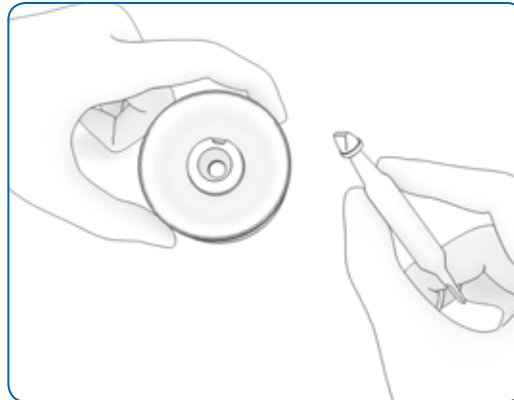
Installation des Rückschlagventils mithilfe des Werkzeugs – Teil 1
